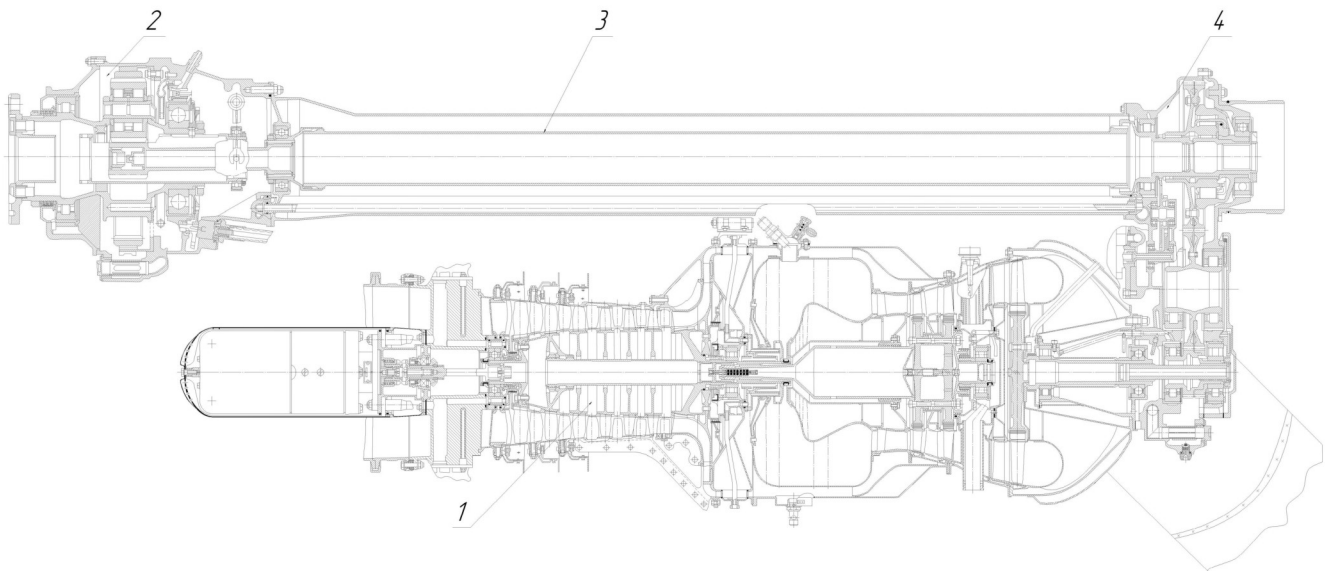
Турбовинтовой двигатель ТВД-10Б с двухступенчатым редуктором
